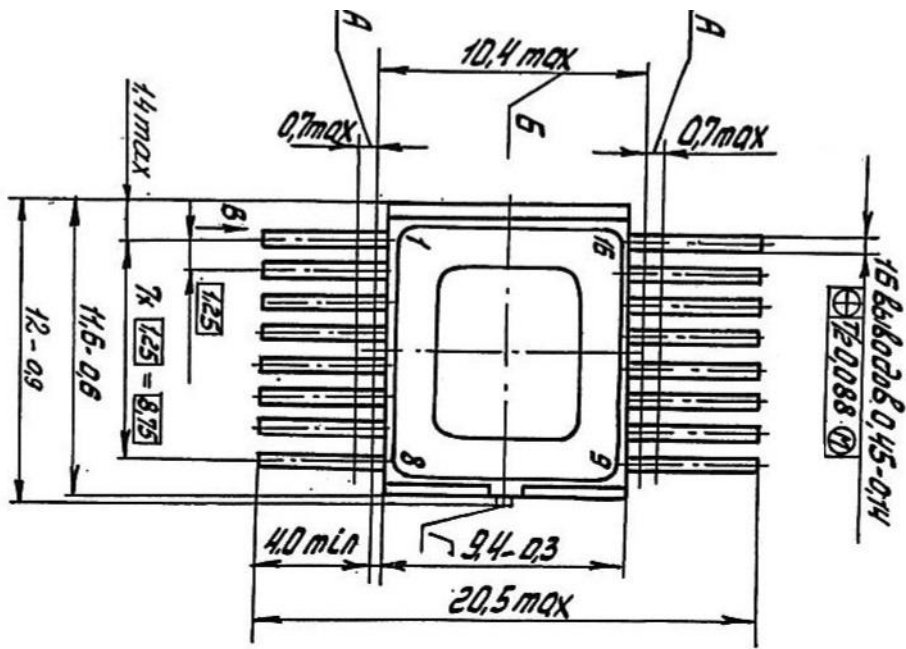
Габаритный чертеж корпуса 4112.16-2
